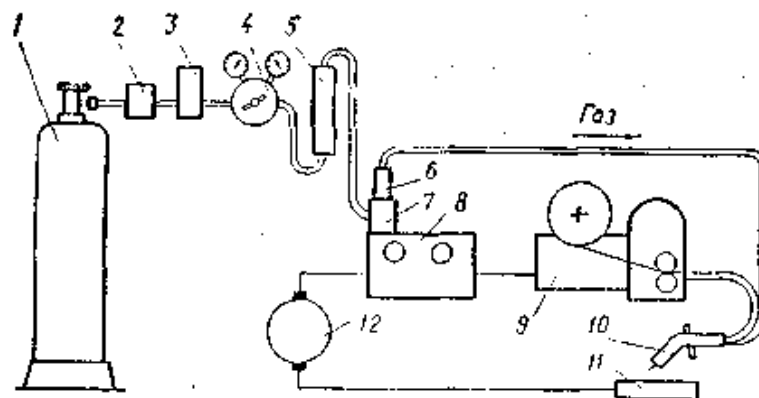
Схема установки для напівавтоматичного зварювання і наплавлення у середовищі вуглекислого газу:
